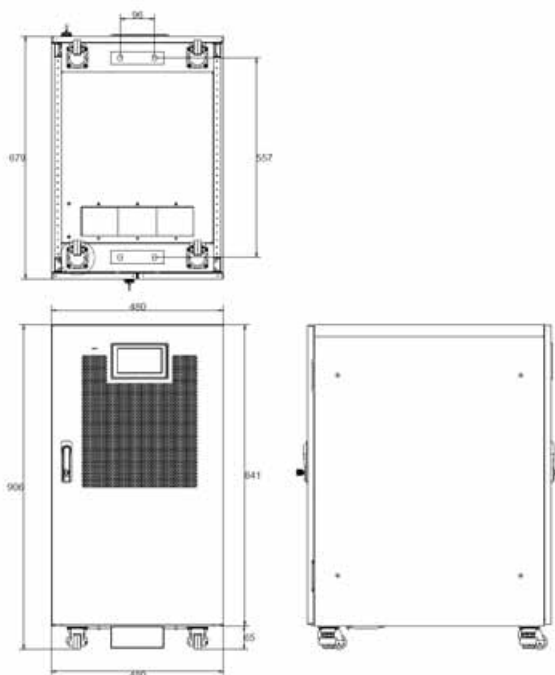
Внешний вид VEDAUPS 90KVA: Габаритный чертёж
